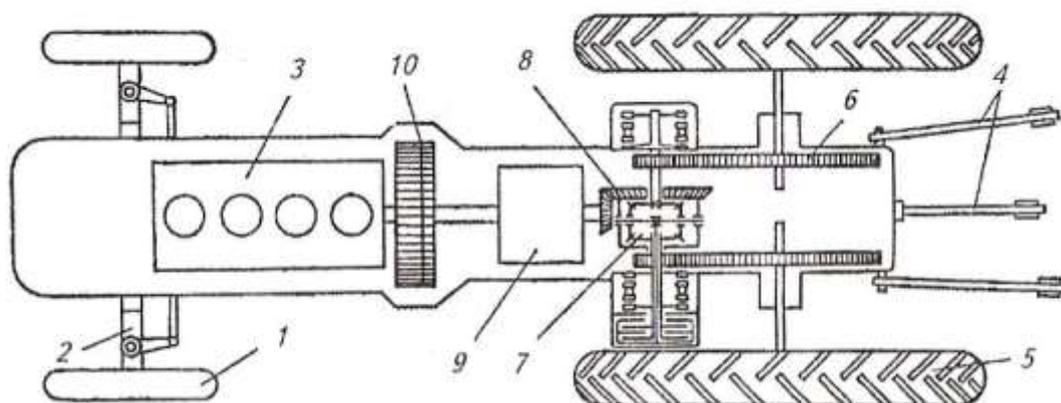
Схема расположения основных частей, механизмов и деталей колесного трактора:
